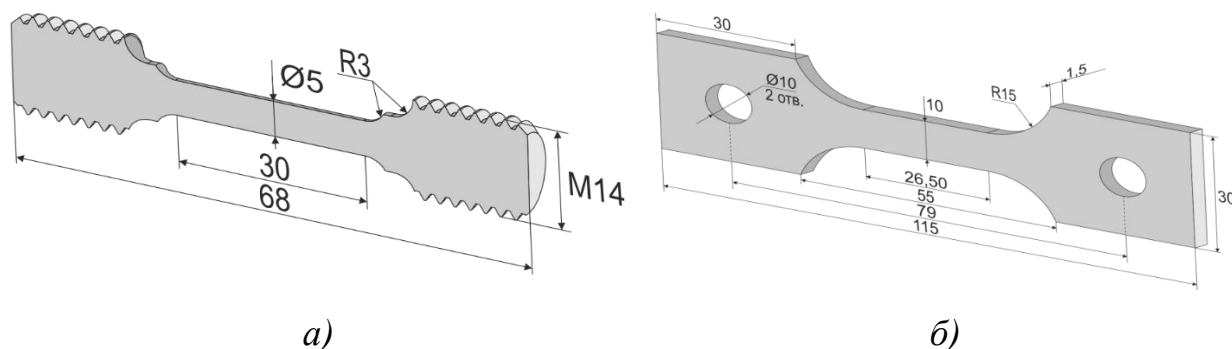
Образцы для испытаний на растяжение и длительную прочность: а) цилиндрический; б) плоский.
